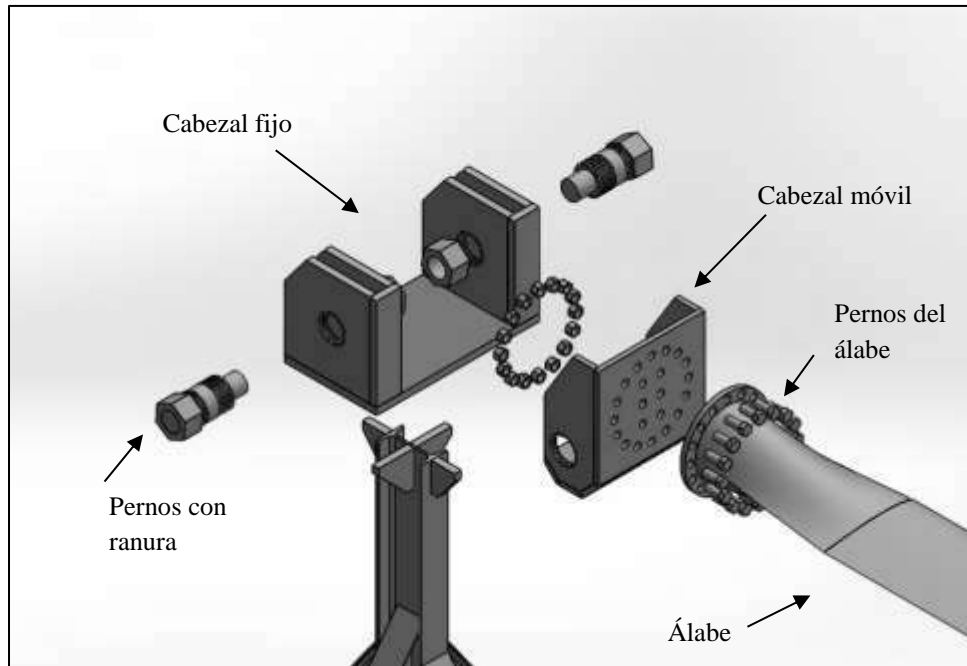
Vista explosionada del cabezal 3. Fuente: SOLIDWORKS 2017.
